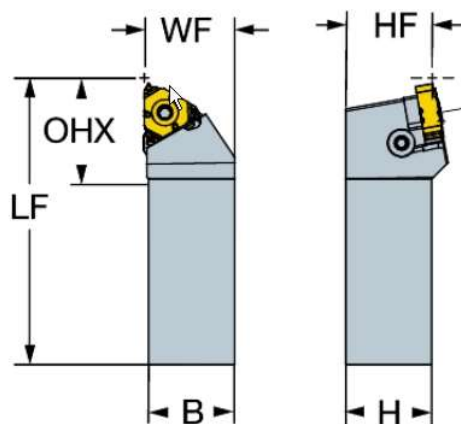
Схематичний вигляд різця «266RFA-2020-16»
